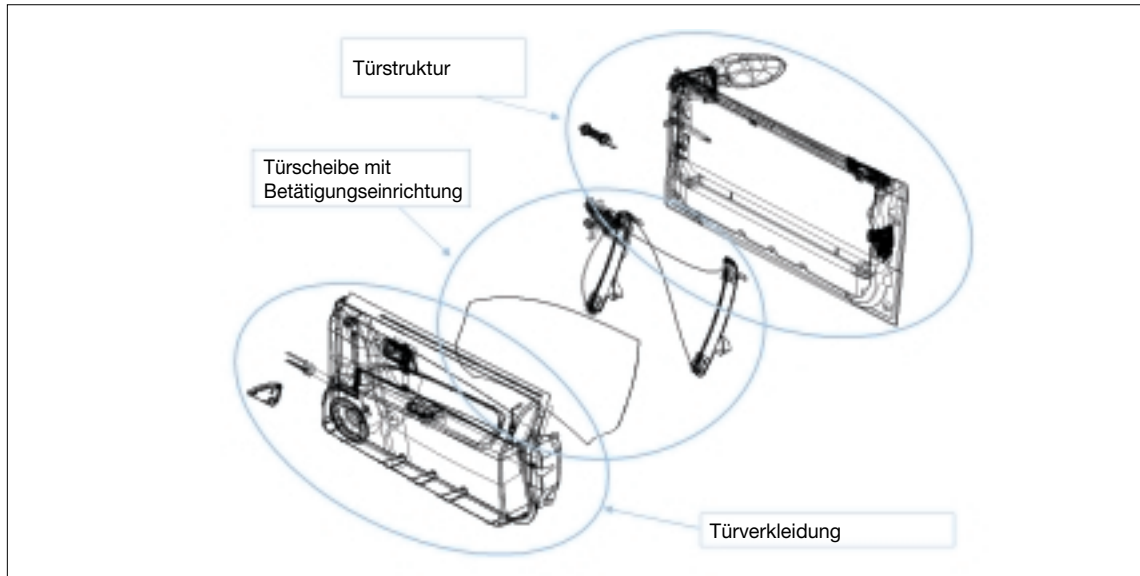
Zusammenbaufolge der Hauptbaugruppen
